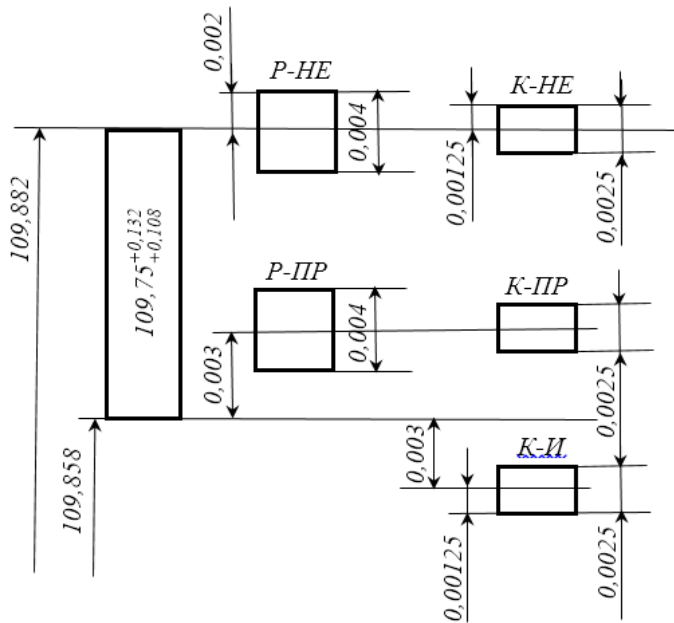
Схема расположения полей допусков калибра-пробки для контроля диаметров коренных опор двигателя ЯМЗ
